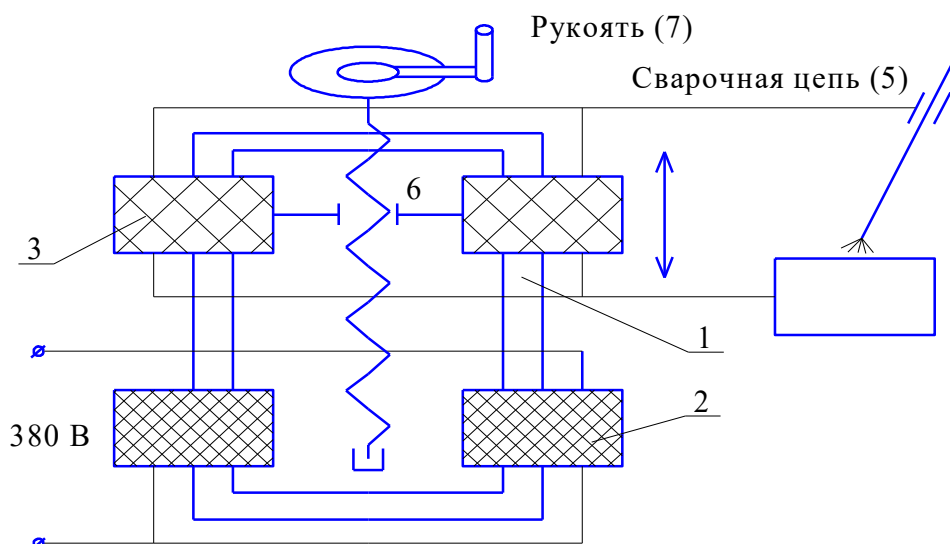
Упрощенная схема сварочного трансформатора с повышенным рассеянием магнитного потока
